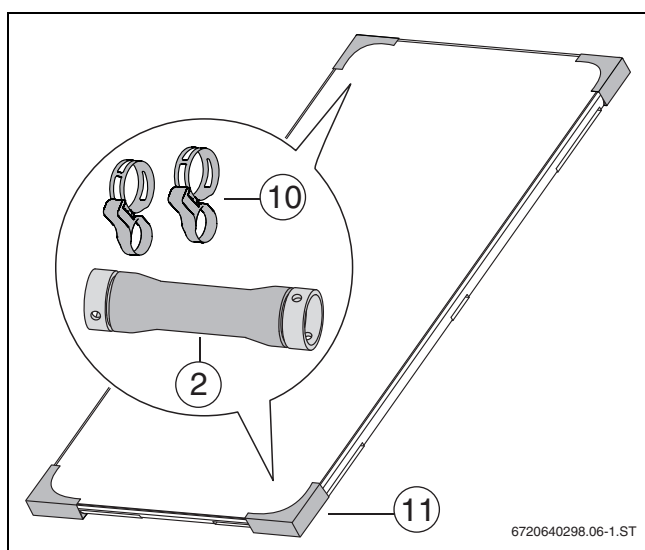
1 zestaw przyłączeniowy do montażu na dachu i 2 zestawy połączeniowe (szare)
